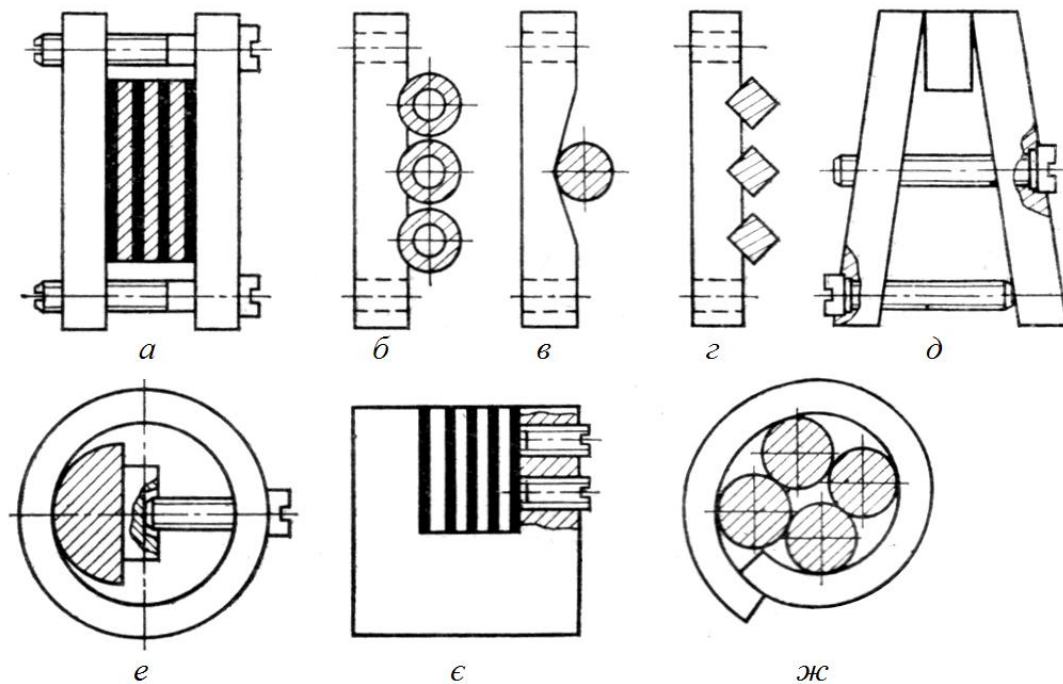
Варіанти розбірних цангових затискачів для ручного механічного оброблення різної величини зразків з різним поперечним перерізом: а, е – у вигляді тонких пластин; б – трубчатоподібних; в – циліндричного; г – квадратних; д – у вигляді паралелепіпеду; е – сегментоподібного; ж – декількох циліндричних
